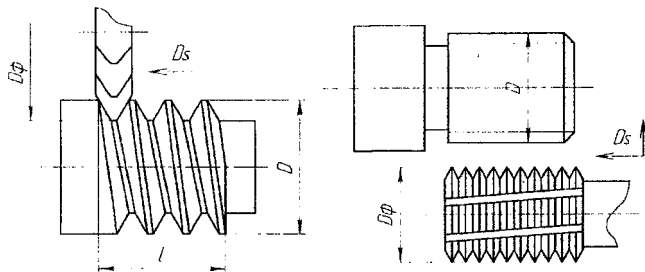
Фрезерование резьбы дисковой и гребенчатой фрезой
